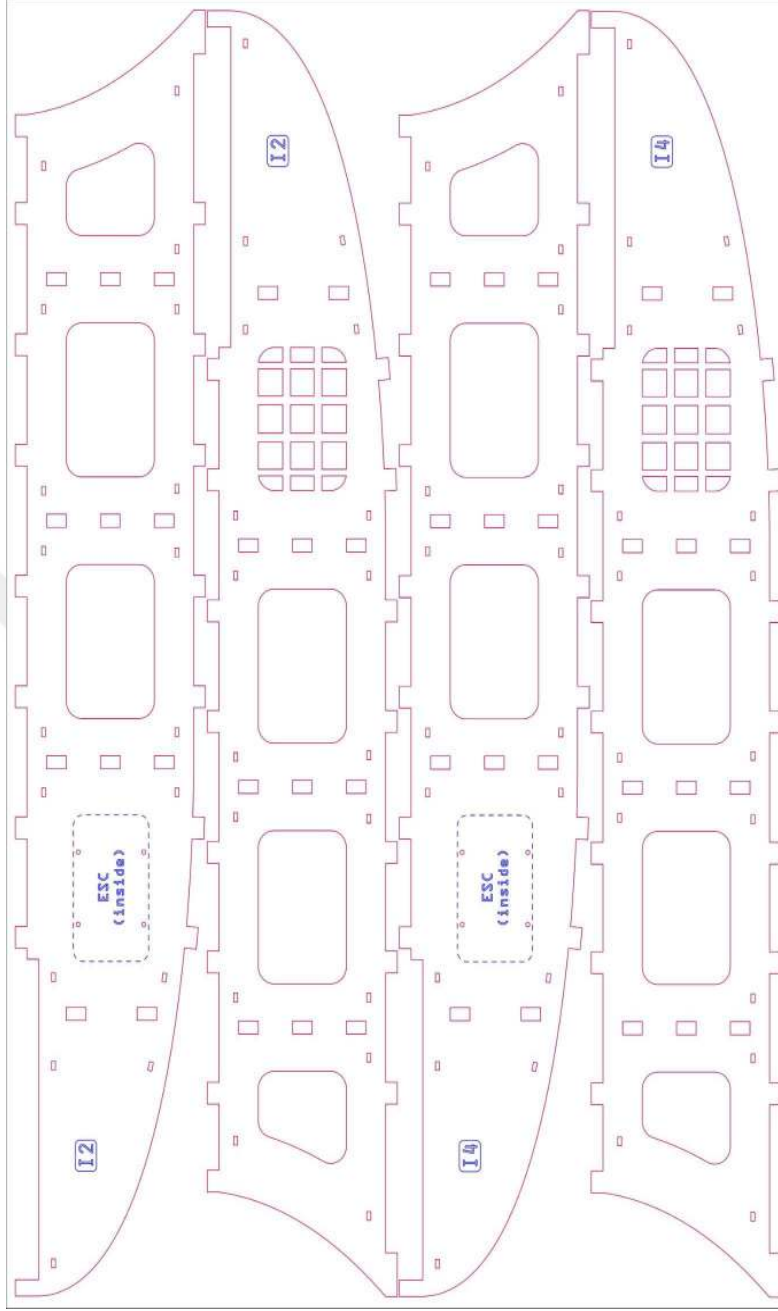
Huş kontrplak malzemenin CNC lazer ile kesimi
